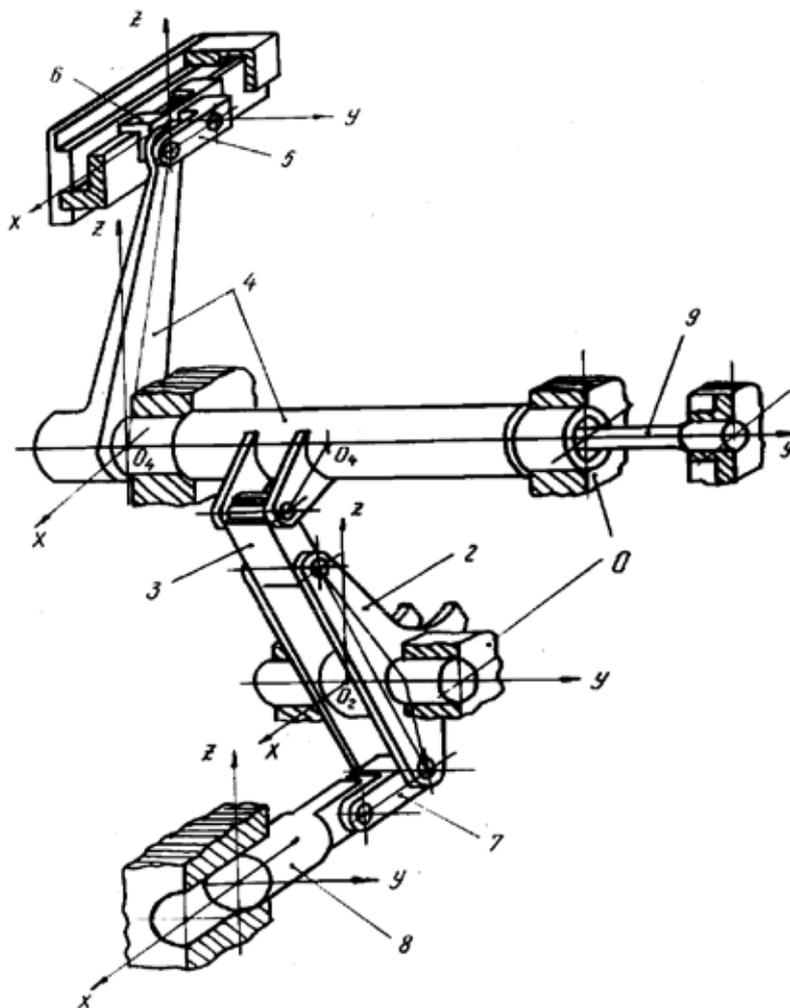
Общий вид и конструкция боевого механизма станков-автоматов типа СТБ
